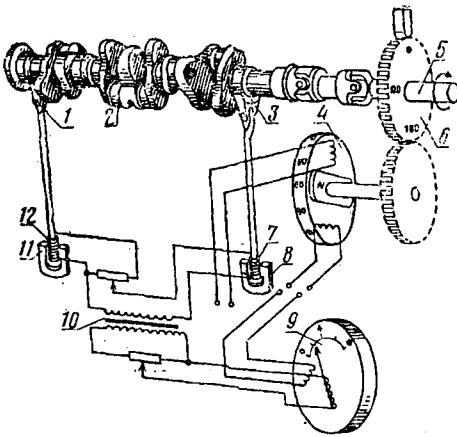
Принципова схема верстата для динамічного балансування колінчастих валів: 1 і 3 – опори; 2 – балансуємий колінчастий вал; 4 – генератор; 5 – приводний вал; 6 – зубчате колесо; 7 і 12 – котушки; 8 і 11 – магніти; 9 – прилад для виміру дисбалансу; 10 – підсилювач струму.
